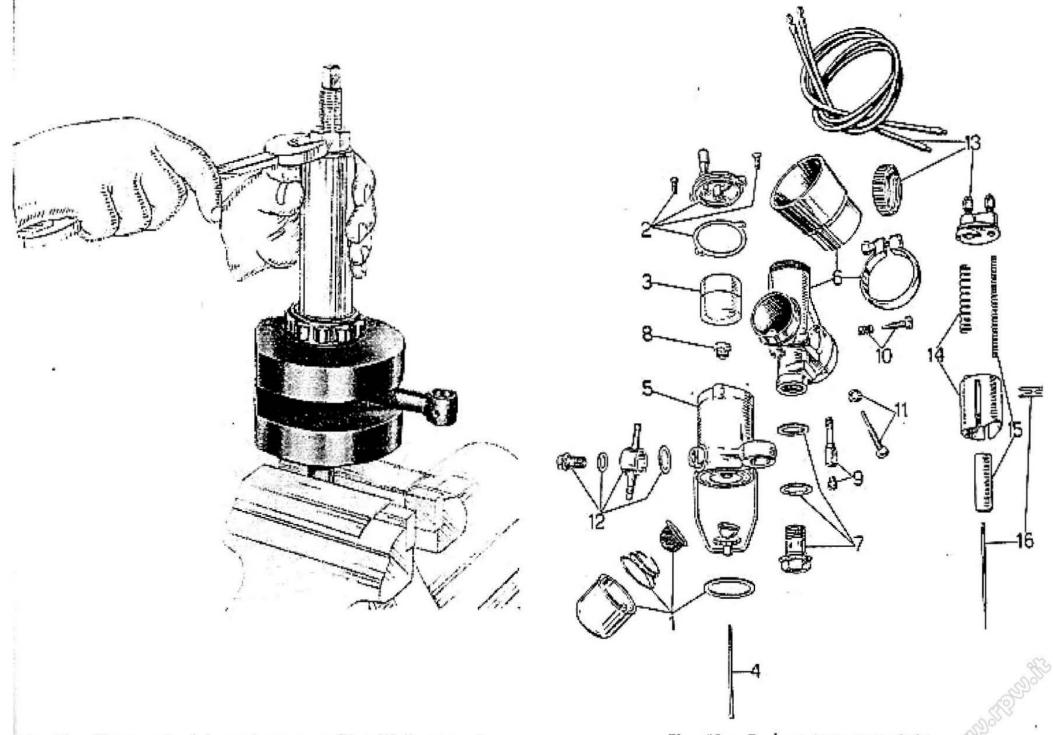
Montaggio del cuscinetto a rulli sull'albero motore.
